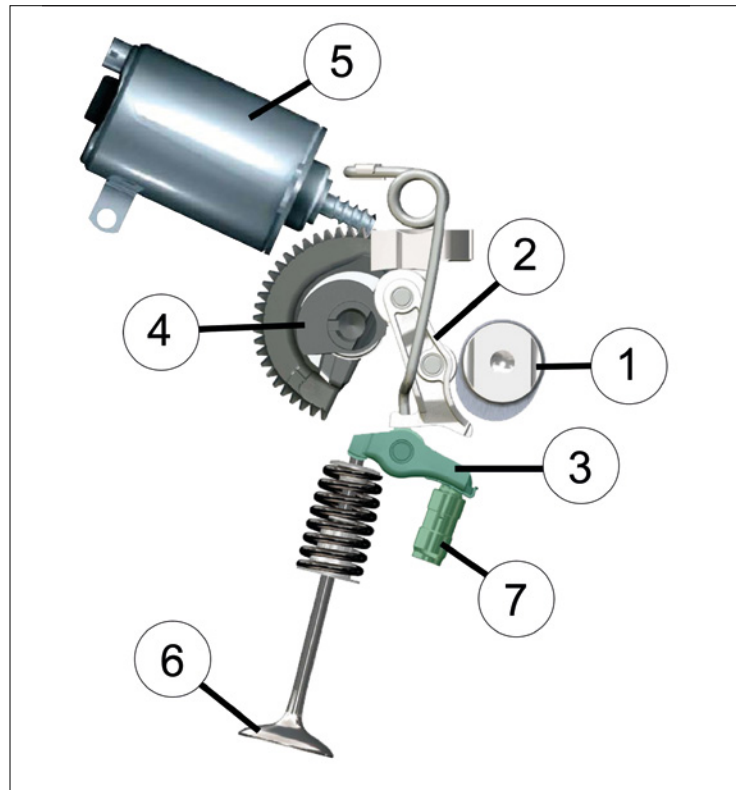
Vista detallada de los componentes del sistema de un motor Valvetronic de BMW
